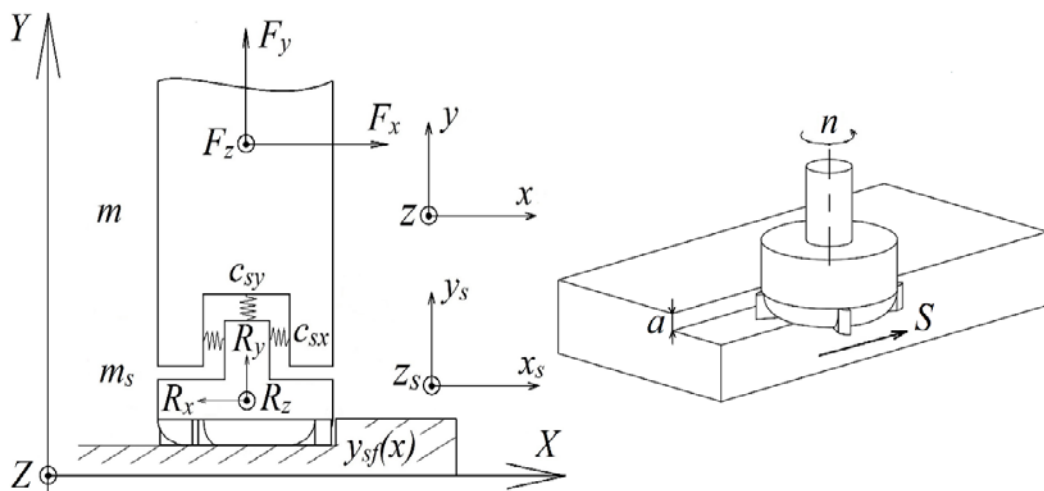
Расчётная схема системы «носитель-инструмент-обрабатываемая поверхность» для процесса фрезерования
